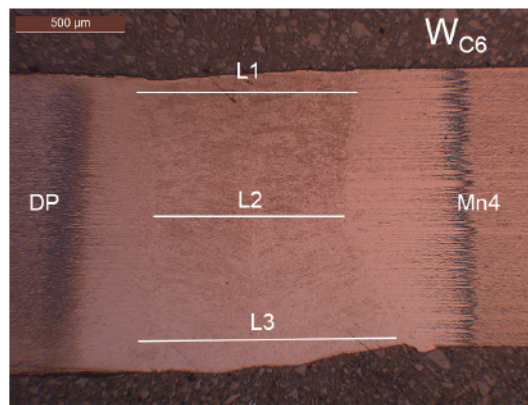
Position des lignes de mesure L1 à L3 pour la mesure de la largeur du joint soudé
